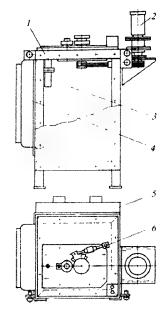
Вальцовочный станок: 1 рама; 2 механизм гибки полос с приволом; 3 гидропилиндр; 4 пульт управления; 5 писвмогидропанели; 6 паправляющее устройство
